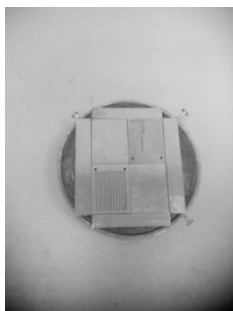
Заготовки и "паразитные" детали на планшайбе до обработки
